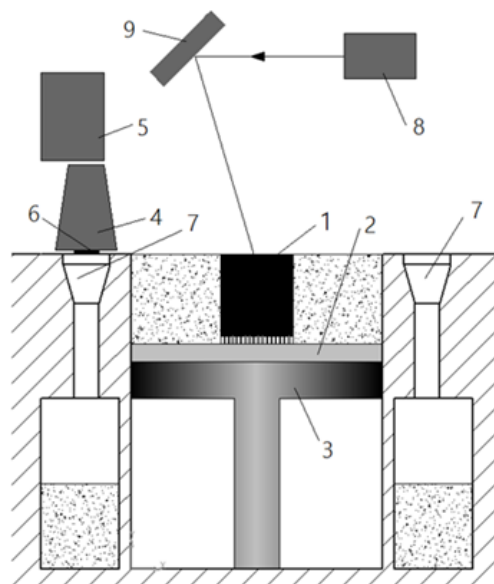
Установка селективного лазерного сплавления SLM 280HL
